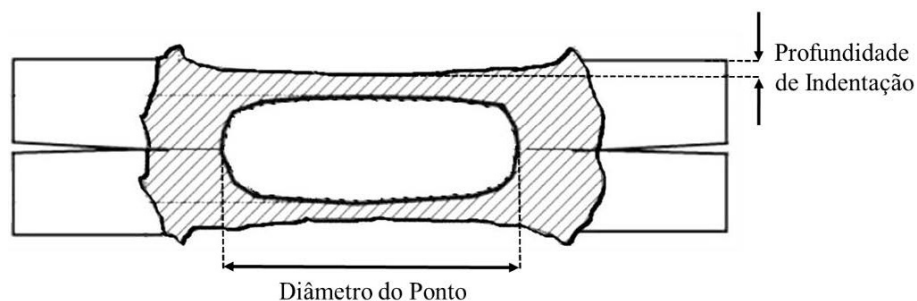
Caracterização geométrica do ponto soldado.
